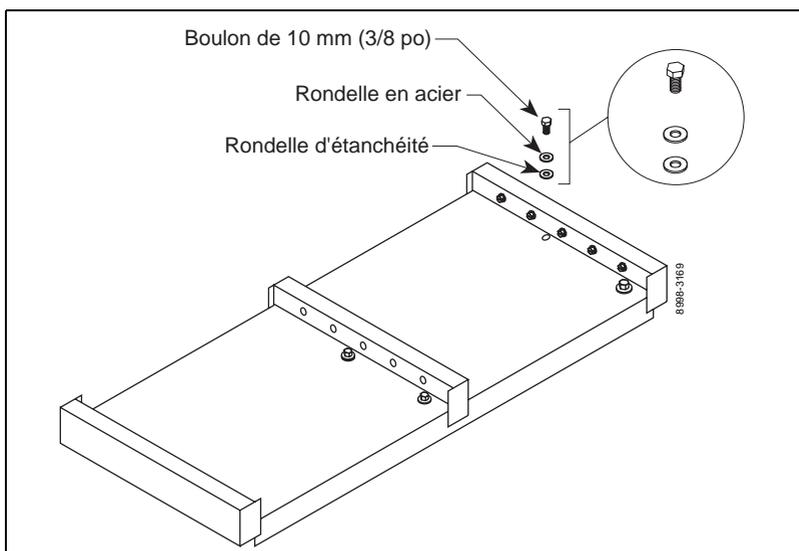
Remise en place de la visserie de la barre de levage angulaire
